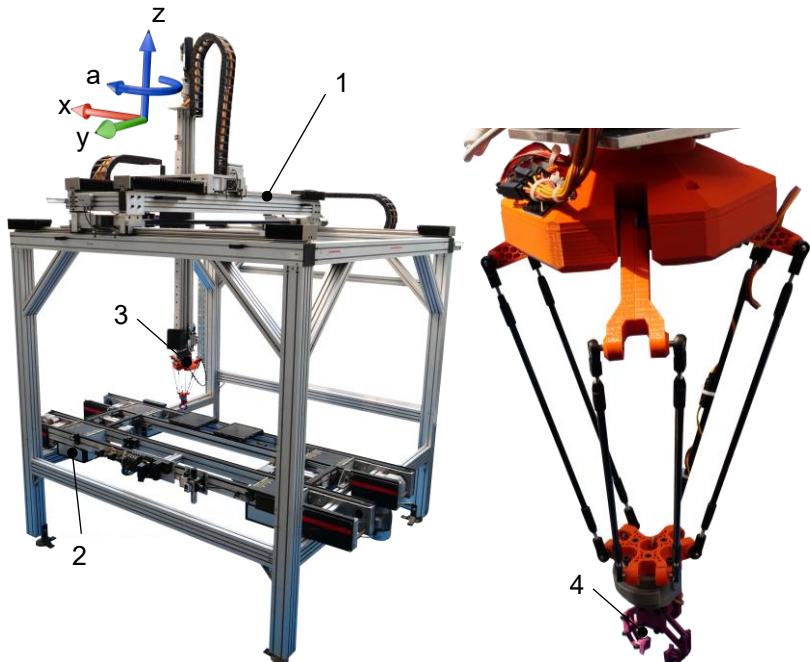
Montagezelle komplett (links), Detailaufnahme Delta-Roboter (rechts)
